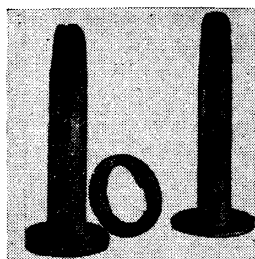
Различные детали, изготовленные из титана ковкой, штамповкой, сваркой и механической обработкой [90].
